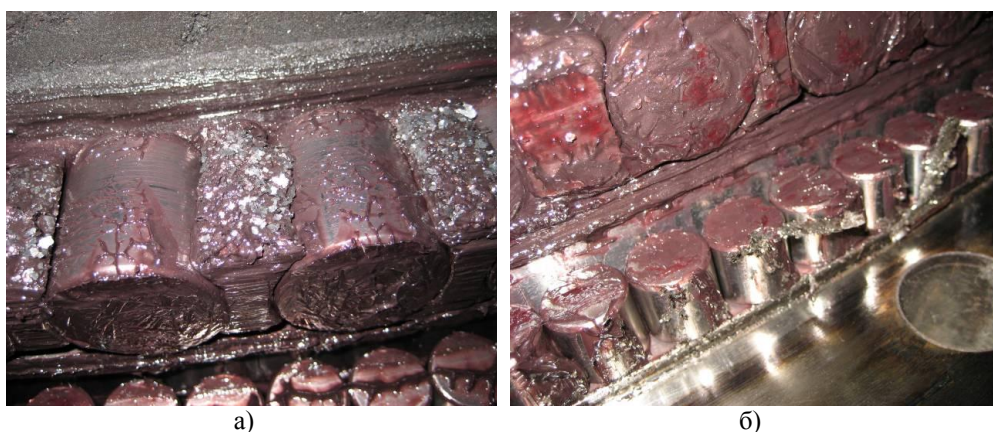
Усталостные трещины поверхностного слоя беговой дорожки подшипника
